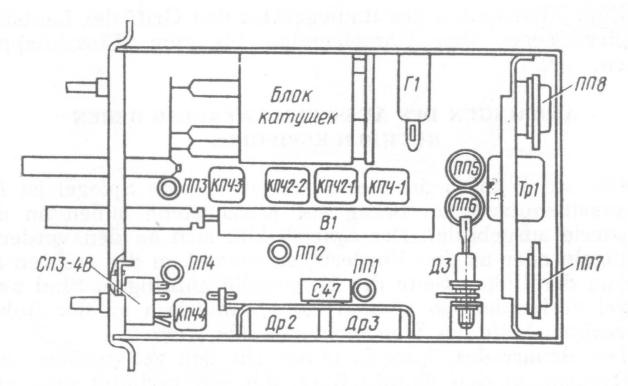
Anordnung der hauptsächlichen Baugruppen und Bauteile des Radiogerätes A-379MI (Draufsicht).
